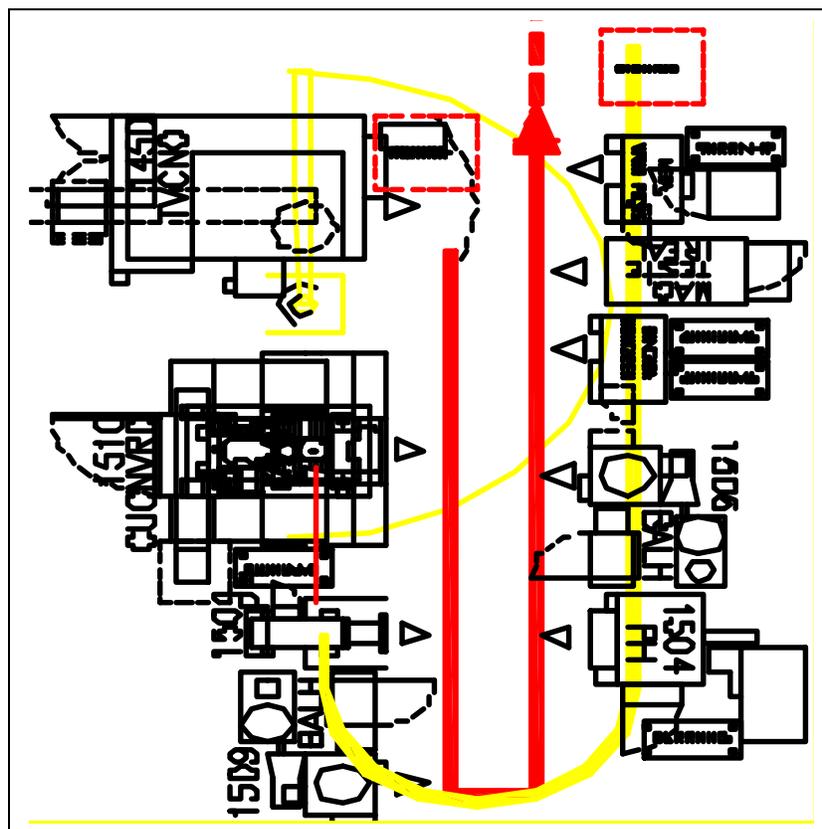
Célula de Usinagem/Montagem de Embreagem
